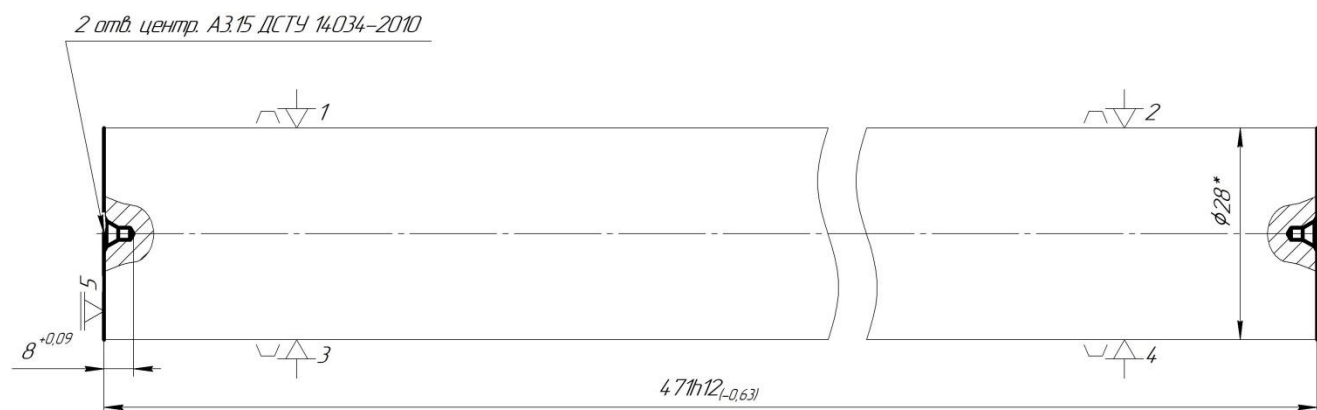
Схема установки заготовки в самоцентрувальні призми
